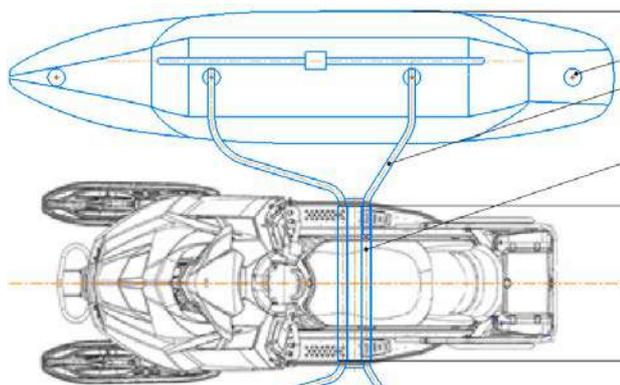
Фрагмент сборочного чертежа приспособления, вид сверху
